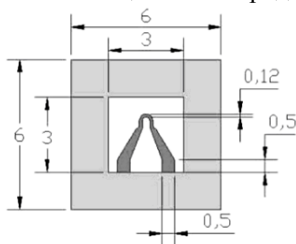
Чертеж микронагревателя (размеры приведены в миллиметрах)
